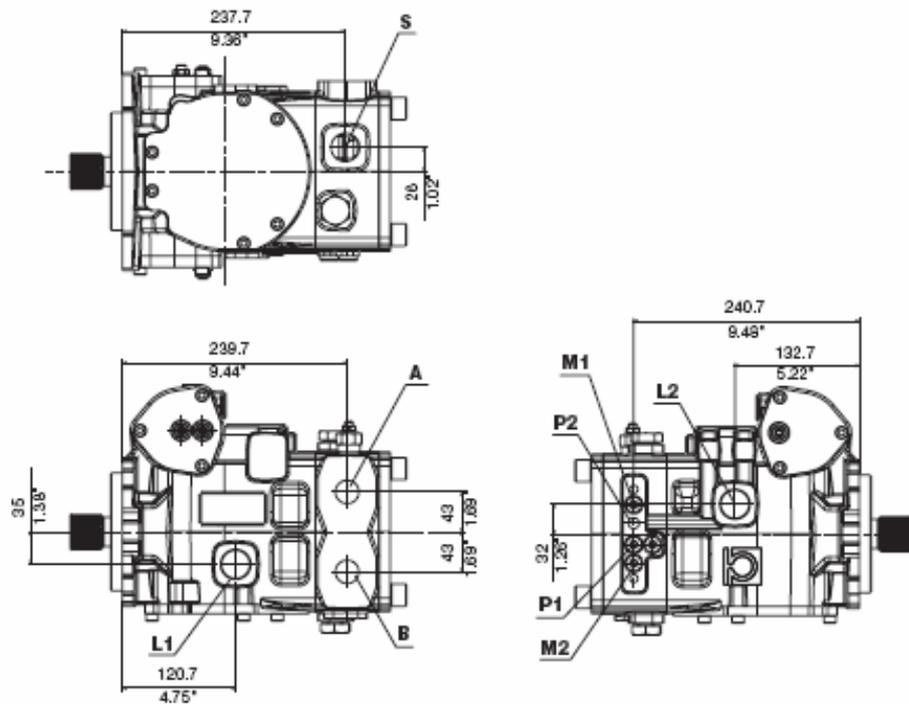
Размеры присоединительных отверстий насосов HP P7 и HP P8.
